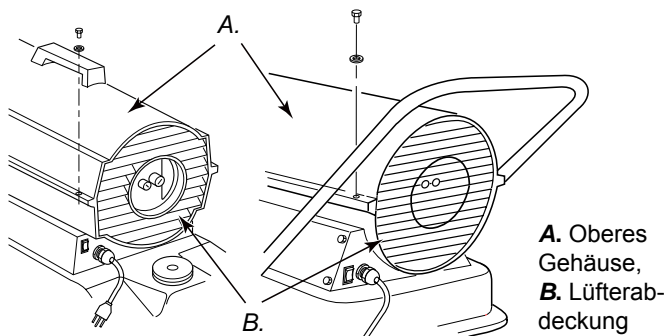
Entfernen des oberen Ge-häuses.
